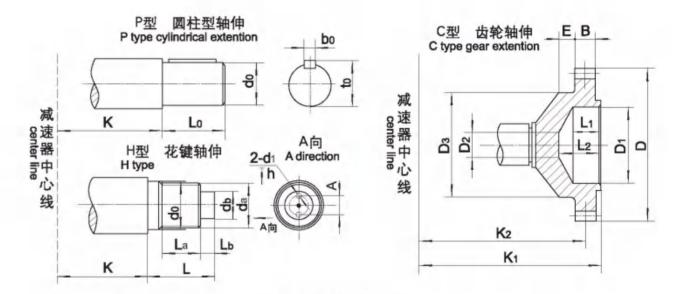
低速轴端型式 Figure 5 Low-speed shaft end form
